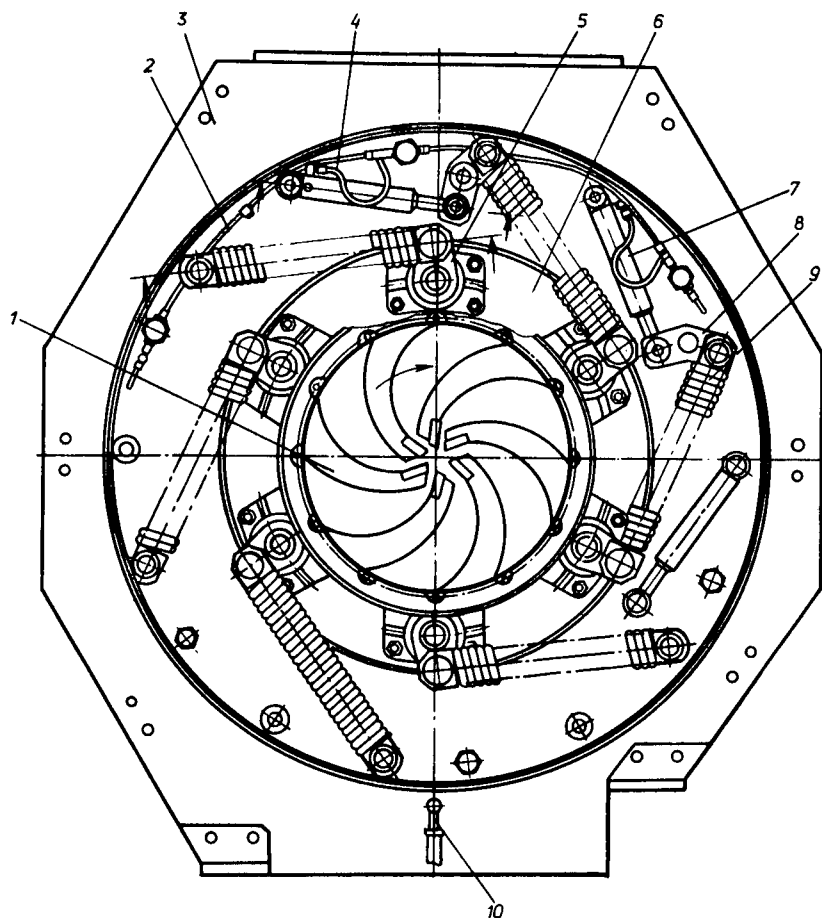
Общий вид станка Камбо 70-65АА:
